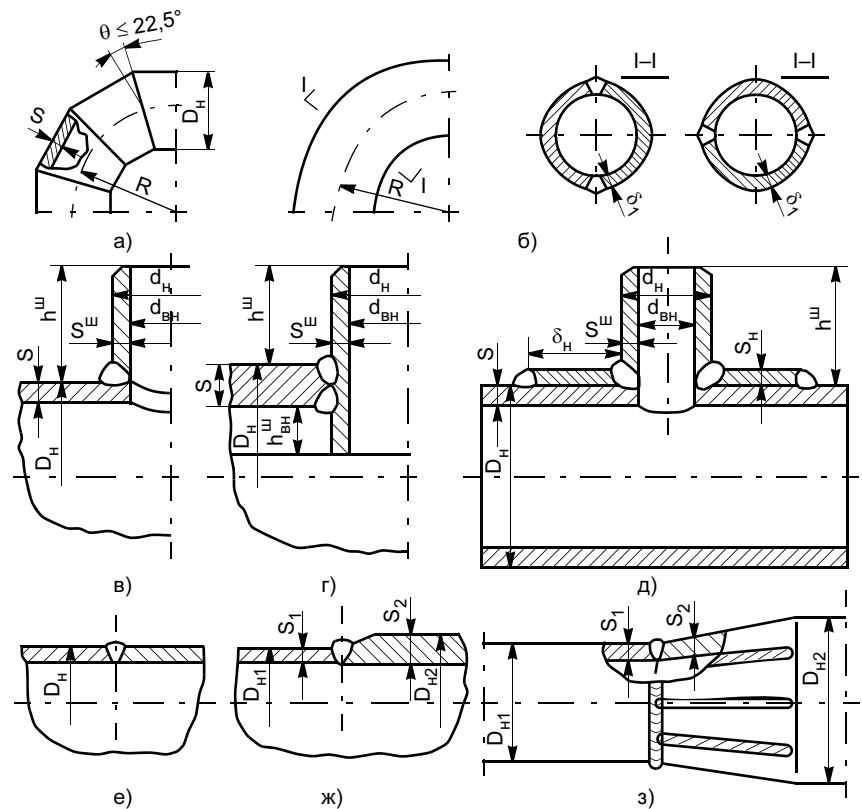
Типы сварных соединений трубопроводов II—IV категорий: а — секторный отвод с поперечными швами; б — штампованное колено (ШСК) с продольными швами; в—д — тройниковые сварные соединения (ТСС) и врезки с угловым швом; е — стыковое сварное соединение равнотолщинных трубных элементов (ССС); ж — стыковое сварное соединение разнотолщинных трубных элементов (СССртэ); з — лепестковый конический переход с продольными швами, приваренный стыковым поперечным швом к трубе
